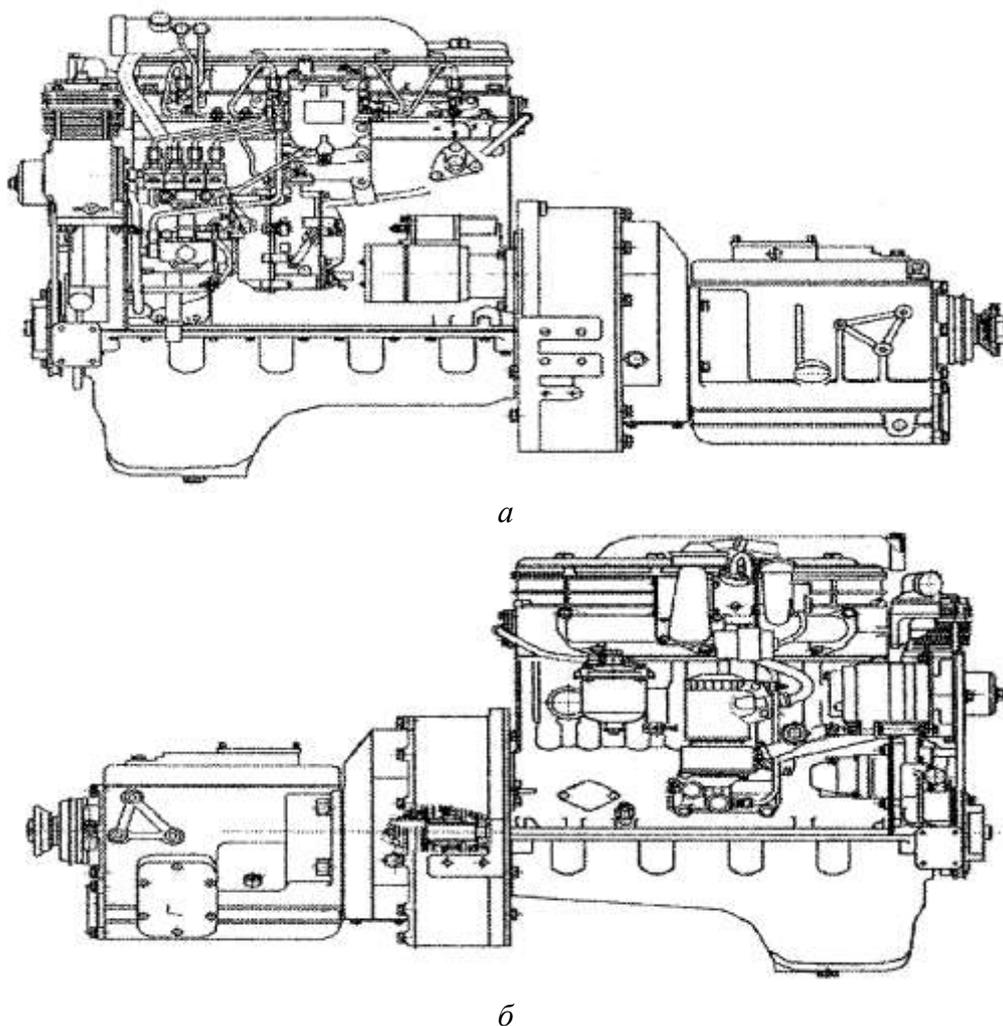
Общий вид дизеля Д-245.30Е2 с муфтой сцепления и коробкой передач:
